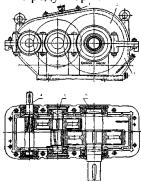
Конструктивная схема двухступенчатого цилиндрического зубчатого редуктора
